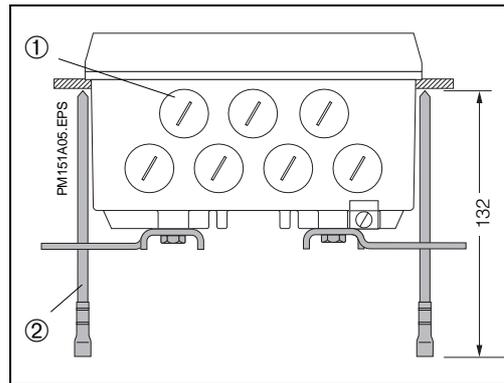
Unterseite des Feldgehäuses mit montierten Spannschrauben zum Schalttafeleinbau
